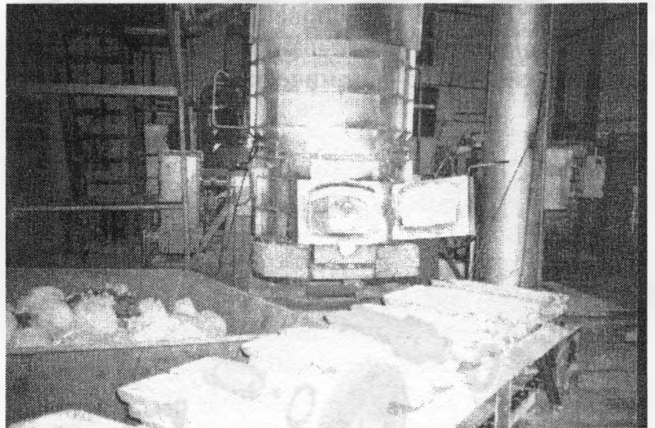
Печь газовая мод. Н318-0000 для переплава шлака
